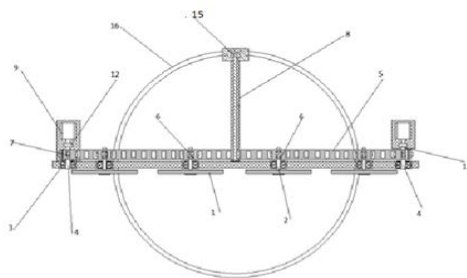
Ветродвижитель с  $N$  ветроколесами (вид сверху)
